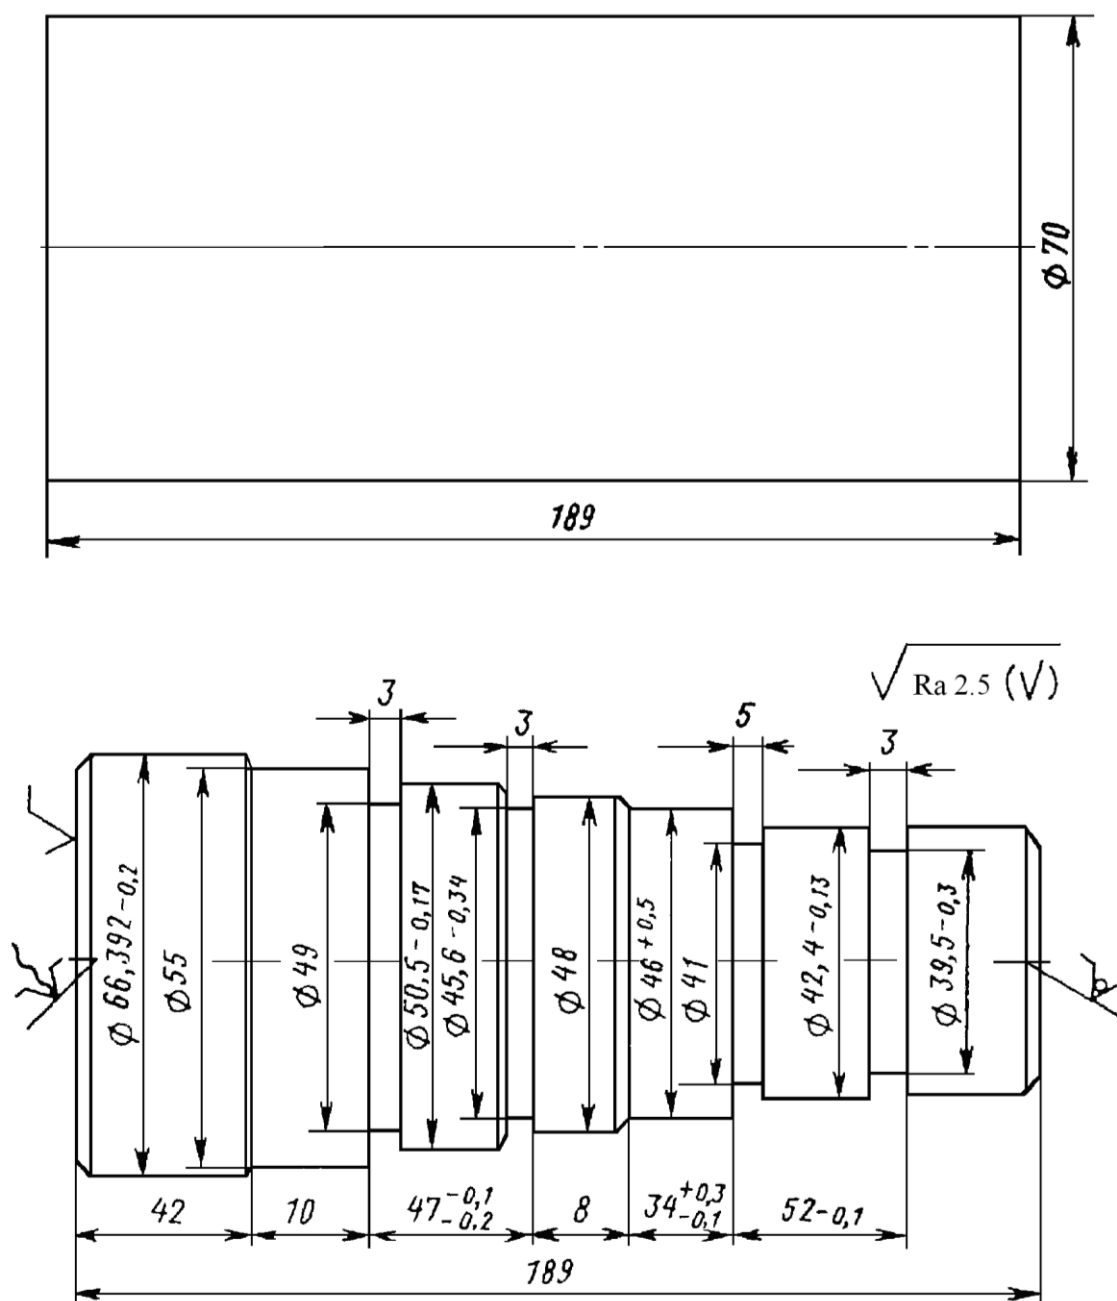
Эскиз заготовки и детали после первой операции технологического процесса изготовления вала-шестерни
